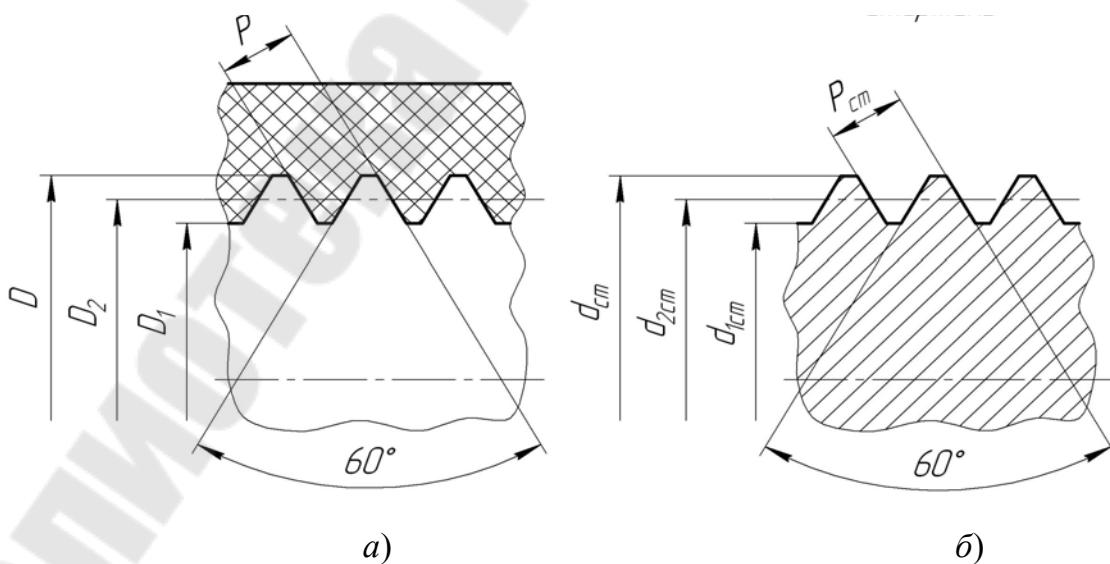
Эскизы: а – гайки; б – резьбооформляющего стержня
